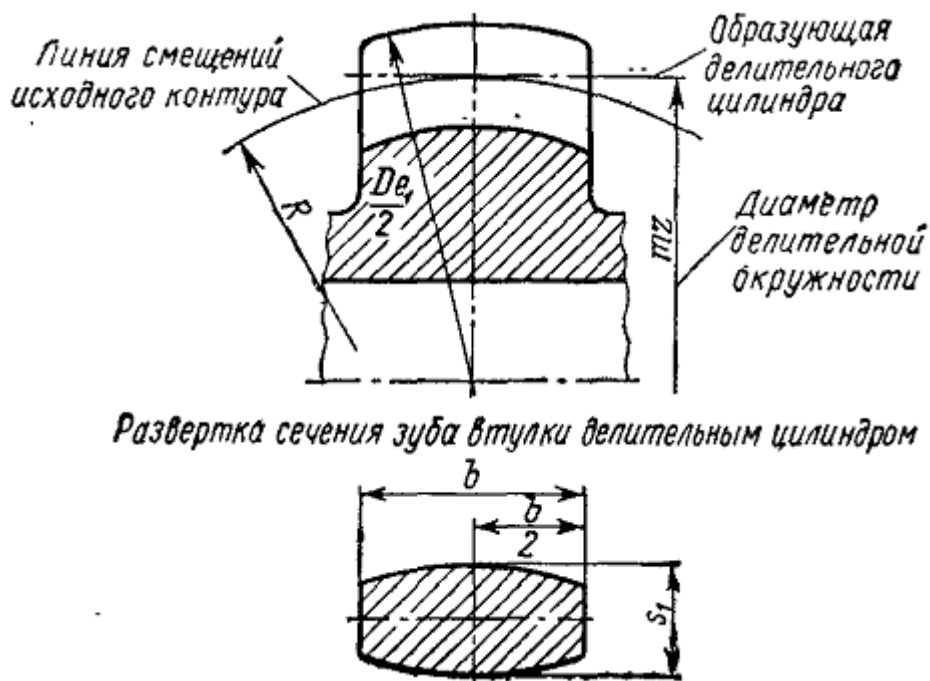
Геометрические размеры бочкообразного зуба зубчатой полумуфты[24]
